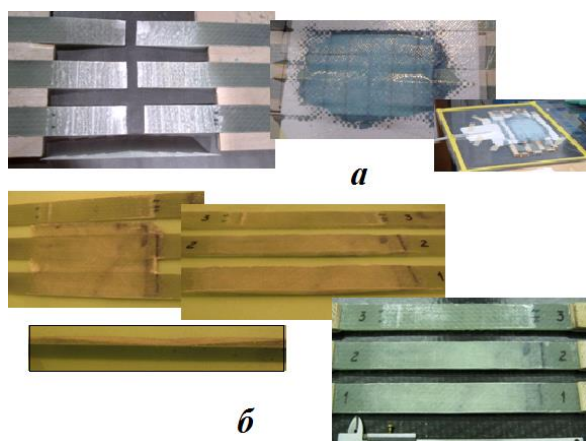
Этапы изготовления ремонтных соединений (а) и изготовление образцов для опытов(б)
